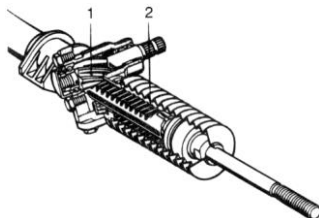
Реечный рулевой механизм: 1 – шестерня; 2 – зубчатая рейка.
